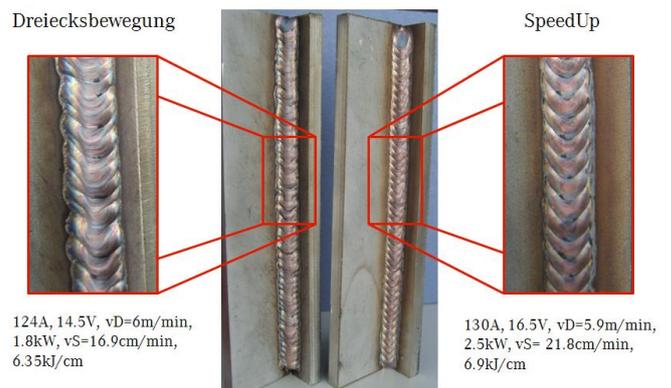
Probe einer Steignachtschweißung an CrNi-Stahl mit der Dreiecksbewegung im direkten Vergleich zur Schweißung mit SpeedUp. Bleche 1.4301 t=8mm, Draht 1mm 1.4316 (ER308) 98%Ar+2%CO₂
